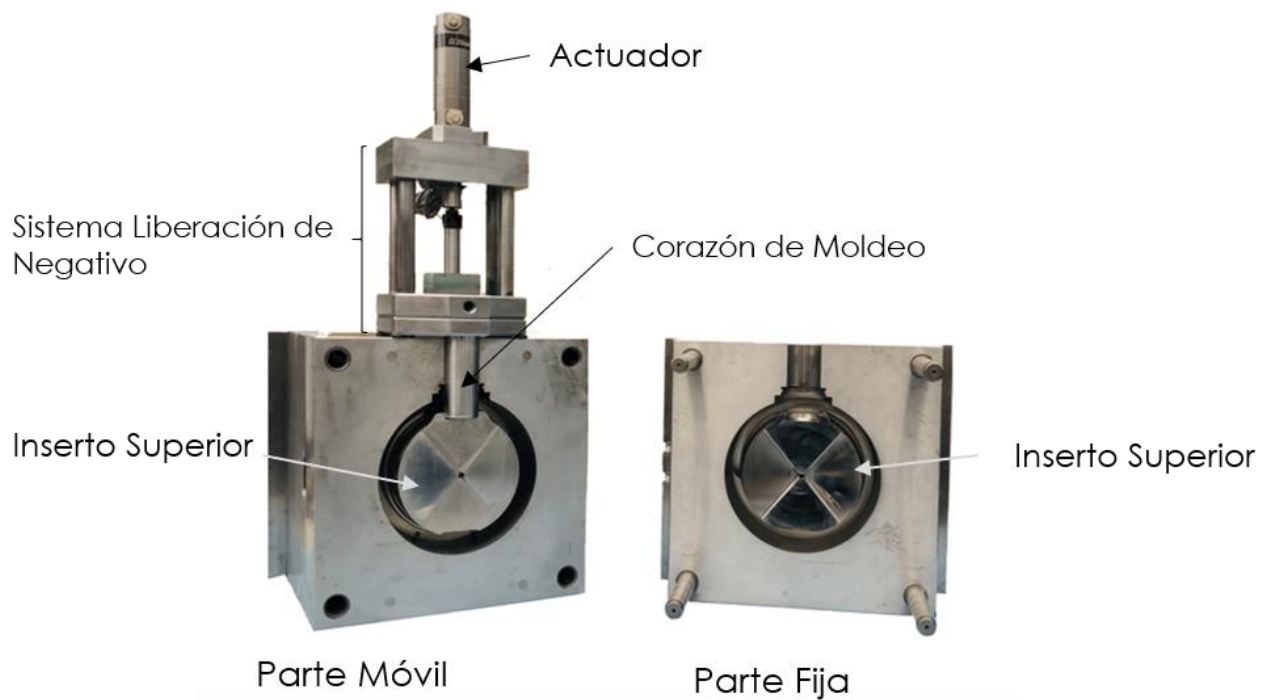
Parte Fija y Móvil de Molde Servo Actuado
